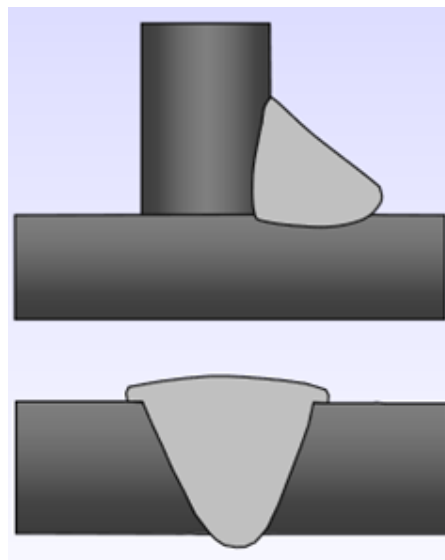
Suprapunerea degetelor de la picioare în sudura cap la cap/filet. Sursă: M.S. Rogers, Welding Inspection Defects/Repairs Course Reference WIS 5, 2003.
